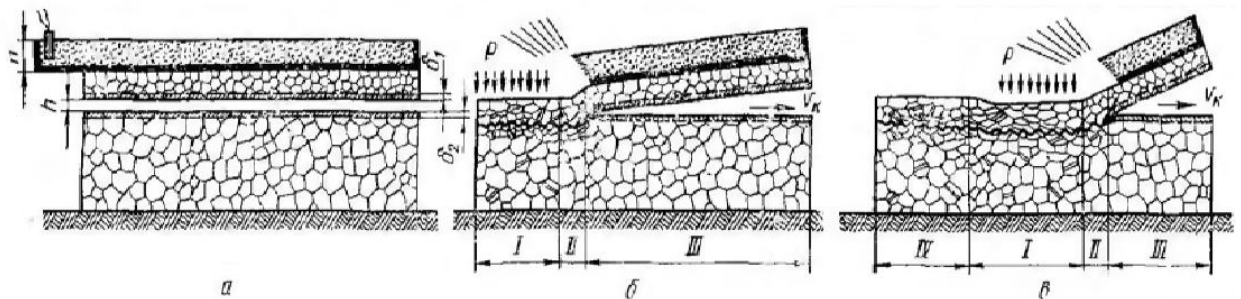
Схема процесу зварювання вибухом під час виготовлення біметалів:
